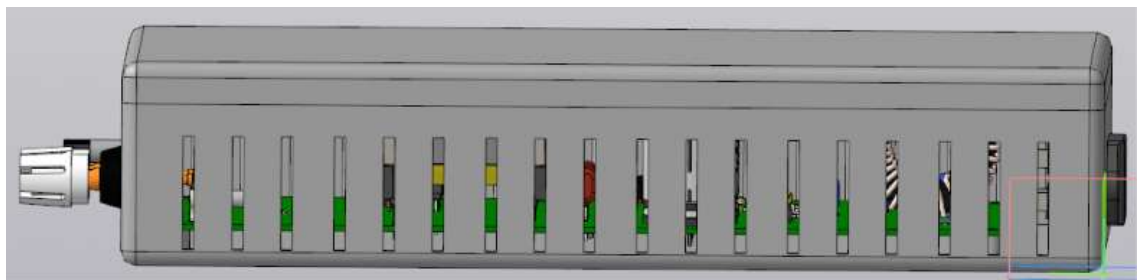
3D модель пристрою в корпусі, вид збоку
